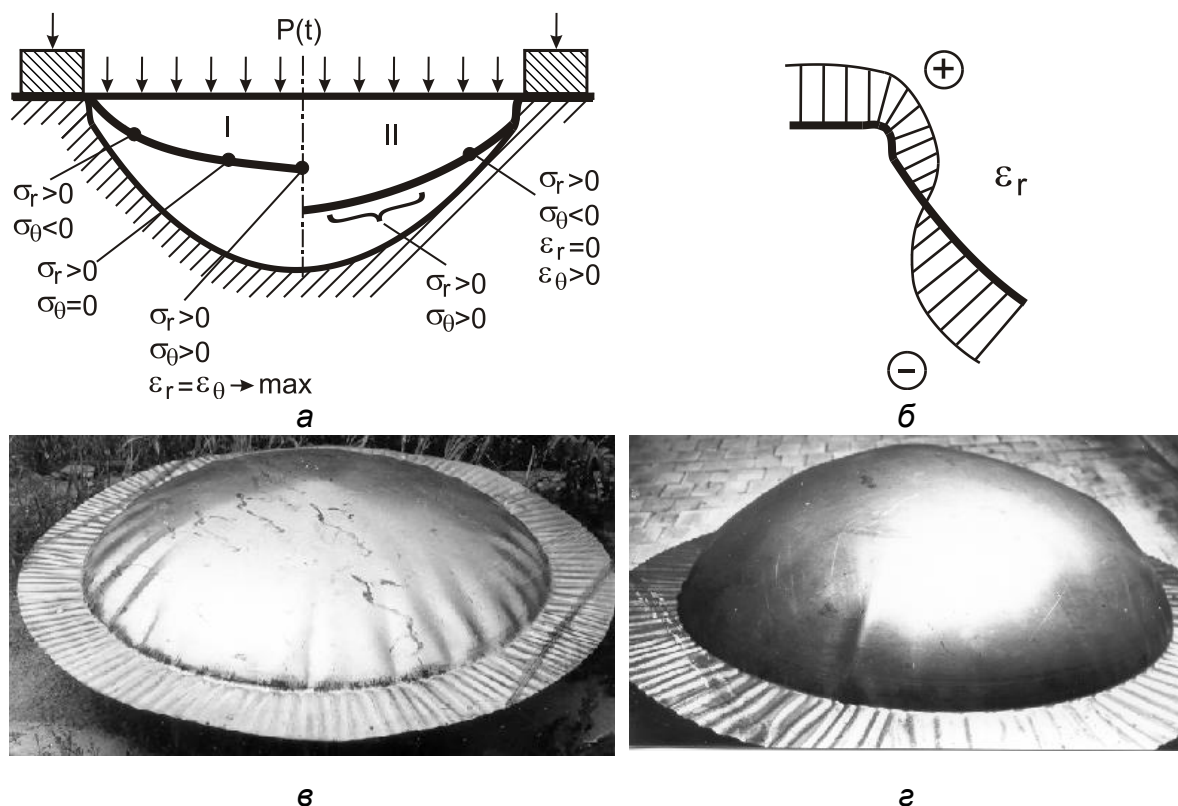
Принципіальна схема штампування-витягування великогабаритного днища імпульсним тиском за всією поверхнею заготовки:
